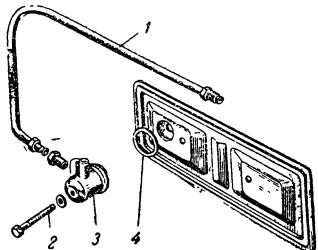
Отсоединение крепления трубы и корпуса клапана вентиляции картера
